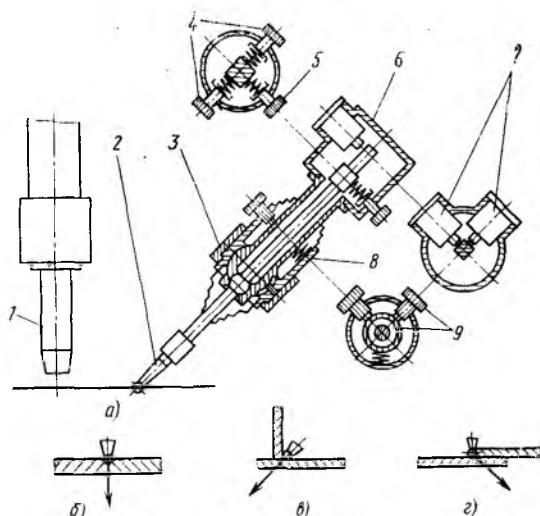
Двухкоординатный электромеханический датчик: а — схема установки; б — направление усилия копирования при сварке стыковых швов; в, г — то же, для угловых швов; 1 — горелка; 2 — щуп; 3 — шарнир поворота щупа в корпусе датчика; 4 — корректоры направления и усилия копирования поперек оси электрода; 5 — корректор копирования вдоль оси электрода; 6 — корпус первичных преобразователей; 7 — первичные преобразователи; 8 — корпус датчика; 9 — корректоры нулевых положений вдоль и поперек оси электрода
